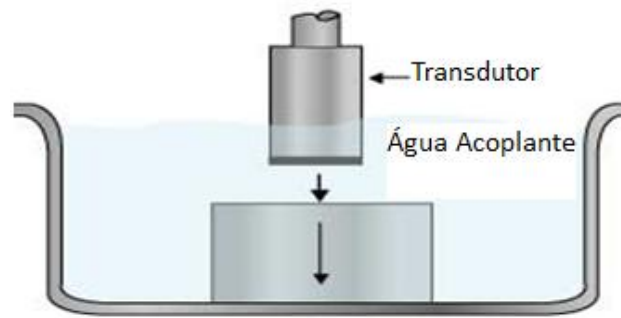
Inspeção realizada com transdutor de imersão [13].
